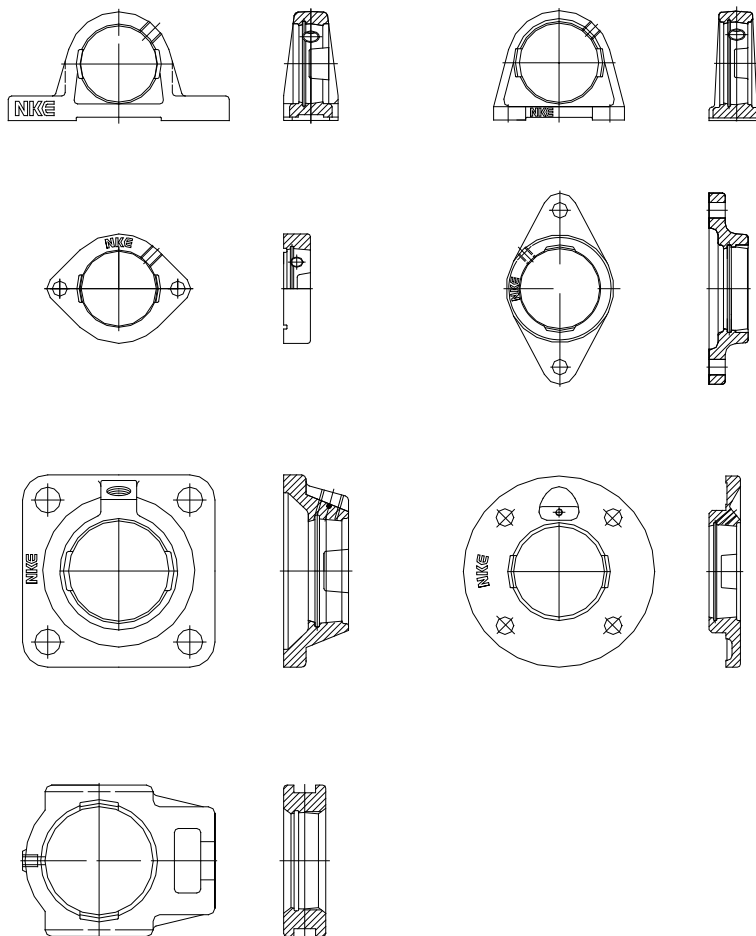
Базовые конструкции стандартных корпусов NKE из чугуна
